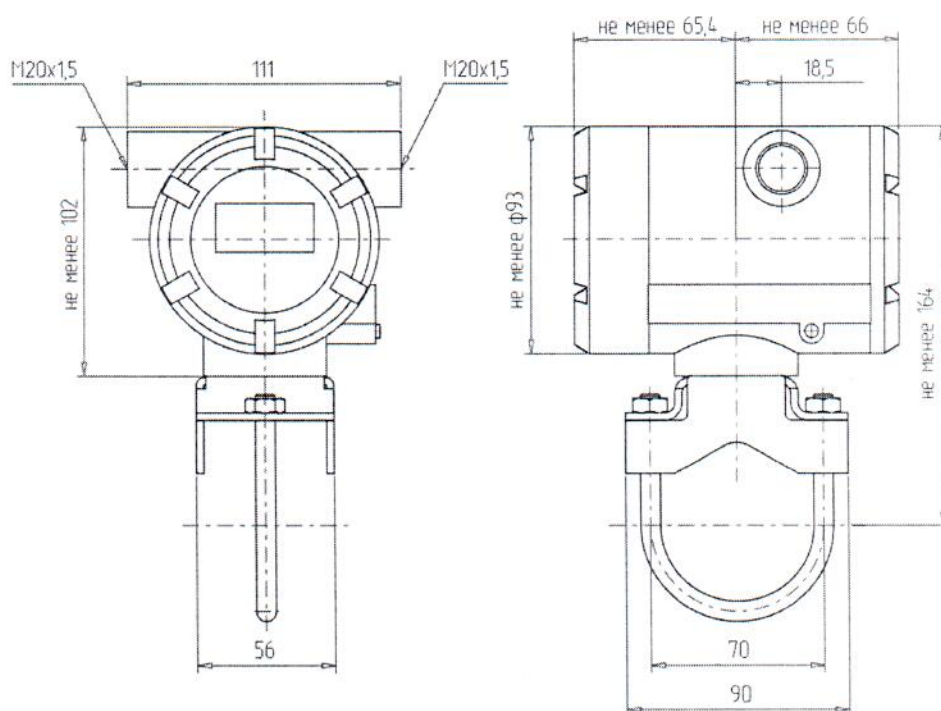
Преобразователь с HART протоколом в корпусе И. Степень защиты оболочки IP68.
